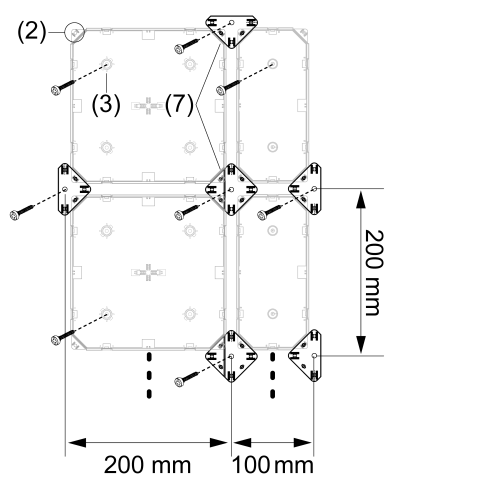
Montage mit Verbindern: LED-Lampe PQ200 und PR100 kombiniert
